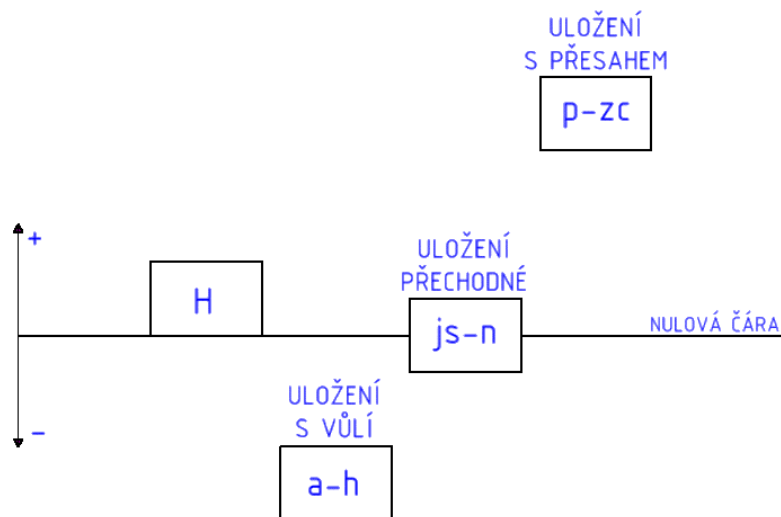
Schématické zobrazení poloh tolerančních polí [5] – upraveno
